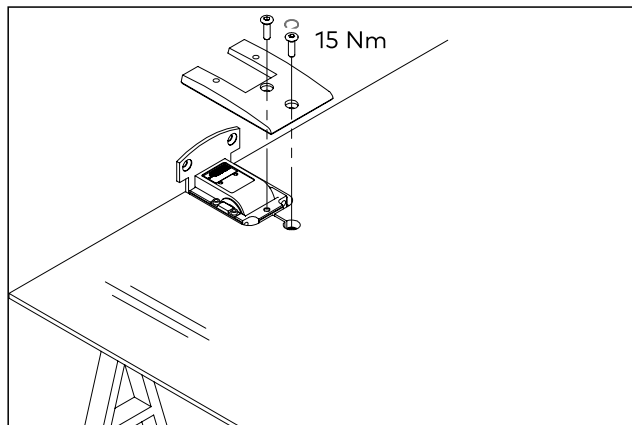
Montage des paumelles à rappel sur le vantail de la porte en verre
